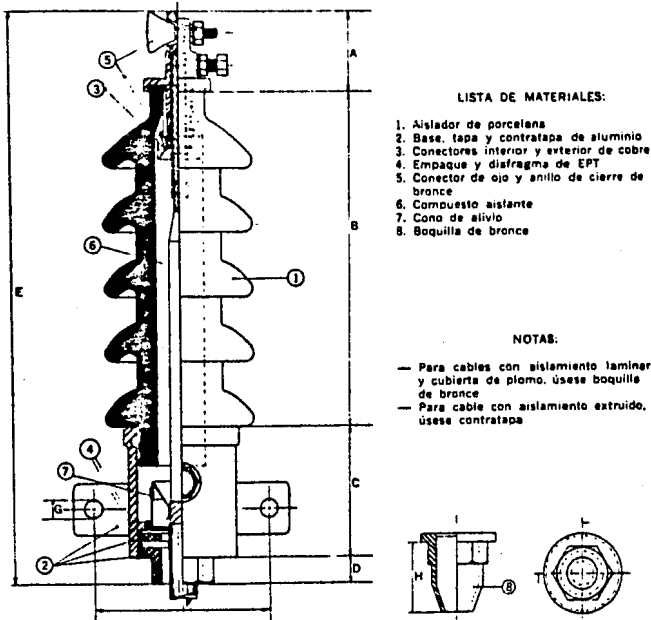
Detalle constructivo de la terminal tipo bayoneta instalada en cable con aislamiento extruido
